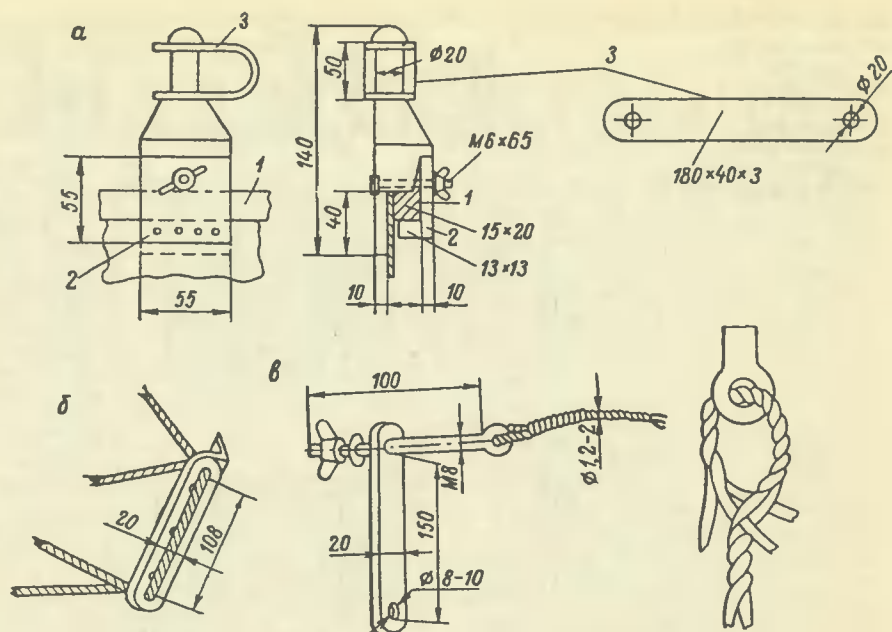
«Ладoga» М1-В. Элементы оборудования: а — передвижная подклочина с резиновой петлей (вид от ДП и в нос), б — металлический уголок на штевне, в — транцевая планка с натяжными винтами; 1 — внутренний привальный брус, 2 — щека с планкой, 3 — резиновая полоса.
